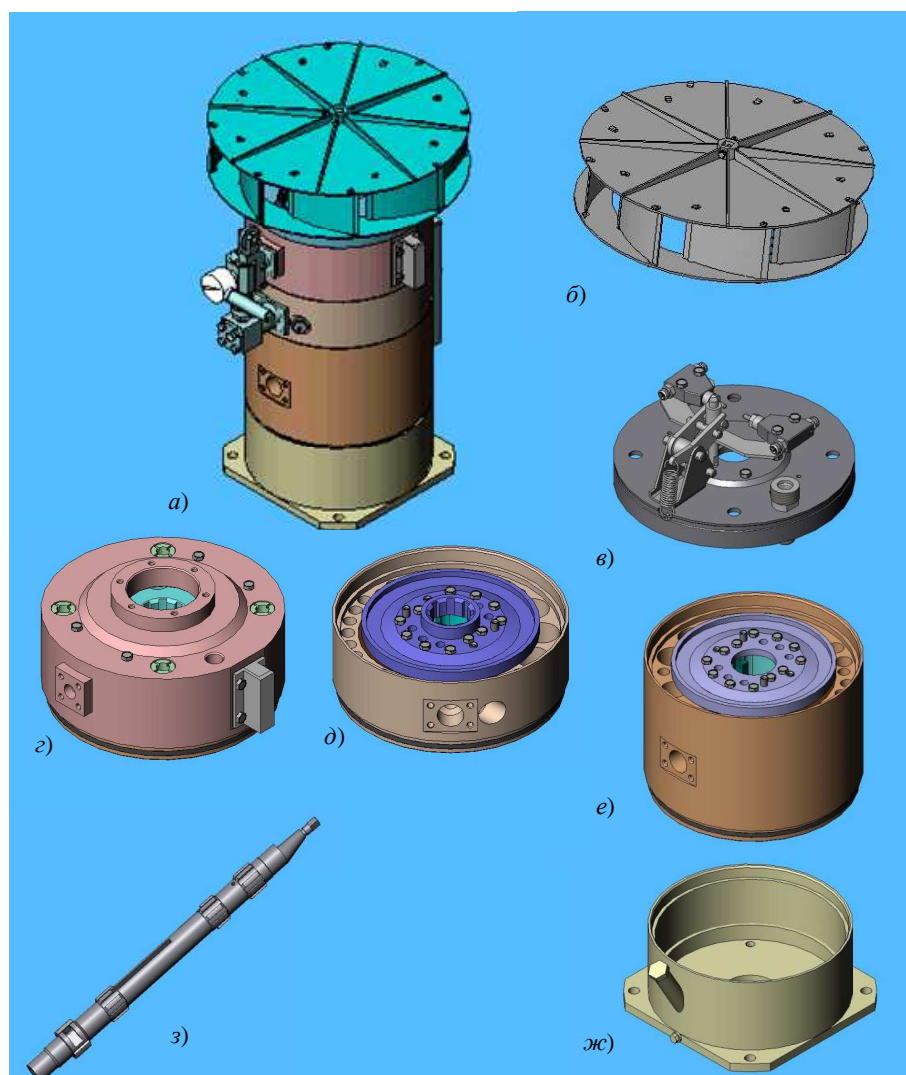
Состав макетного образца ДВС системы «Горник» - а): нагнетатель – (б); секция топливообразующая – (в); компрессор объемный – (г); роторный блок – (д); блок утилизатора – (е); картер - (ж); вал – (з)
